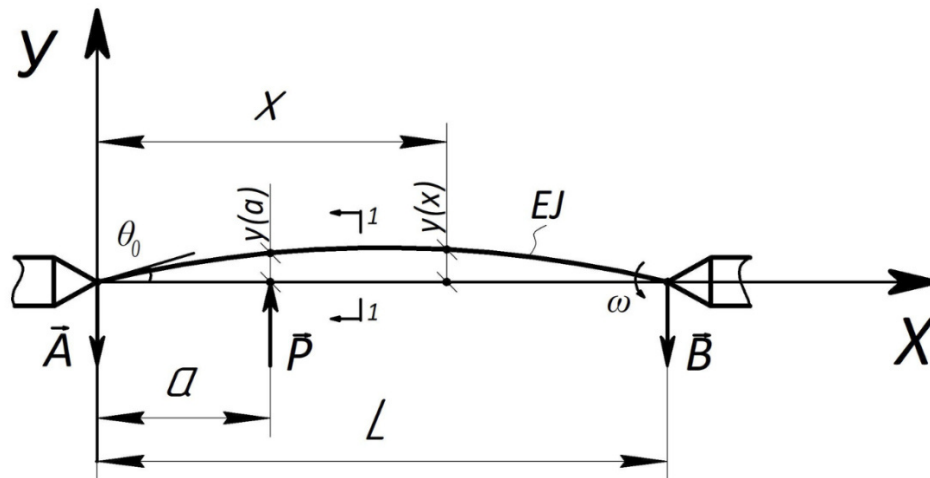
Схема деформирования нежесткой заготовки при токарной обработке
